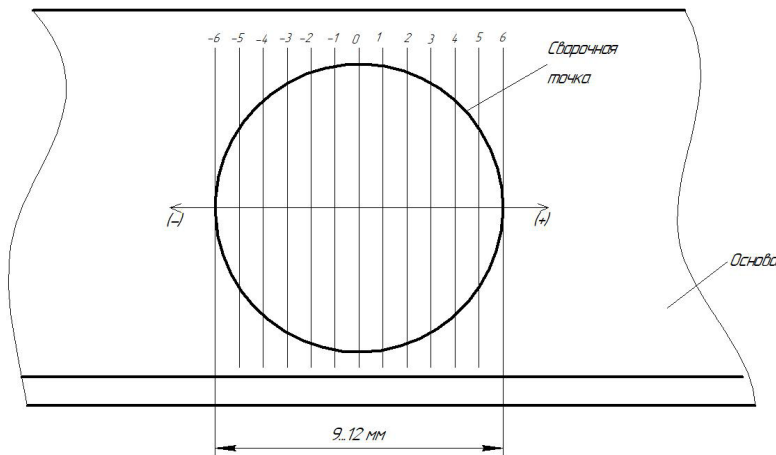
Схема измерения твердости в поперечном направлении сварочной точки
